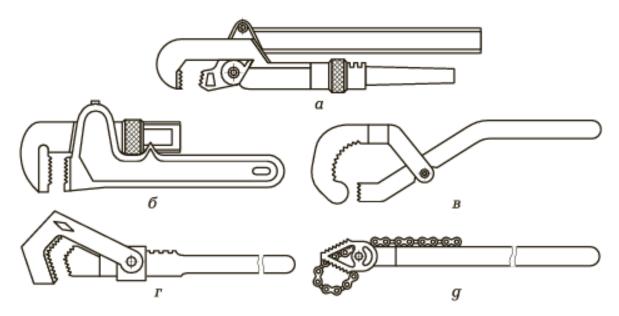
Ключи для сборки трубопроводов: а — рычажный; б — разводной; в — специальный; г — накидной; д — цепной
